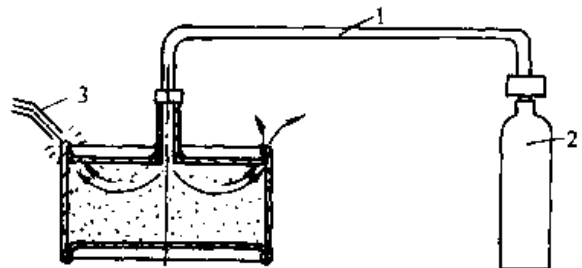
焊接时用惰性气体进行冷却
